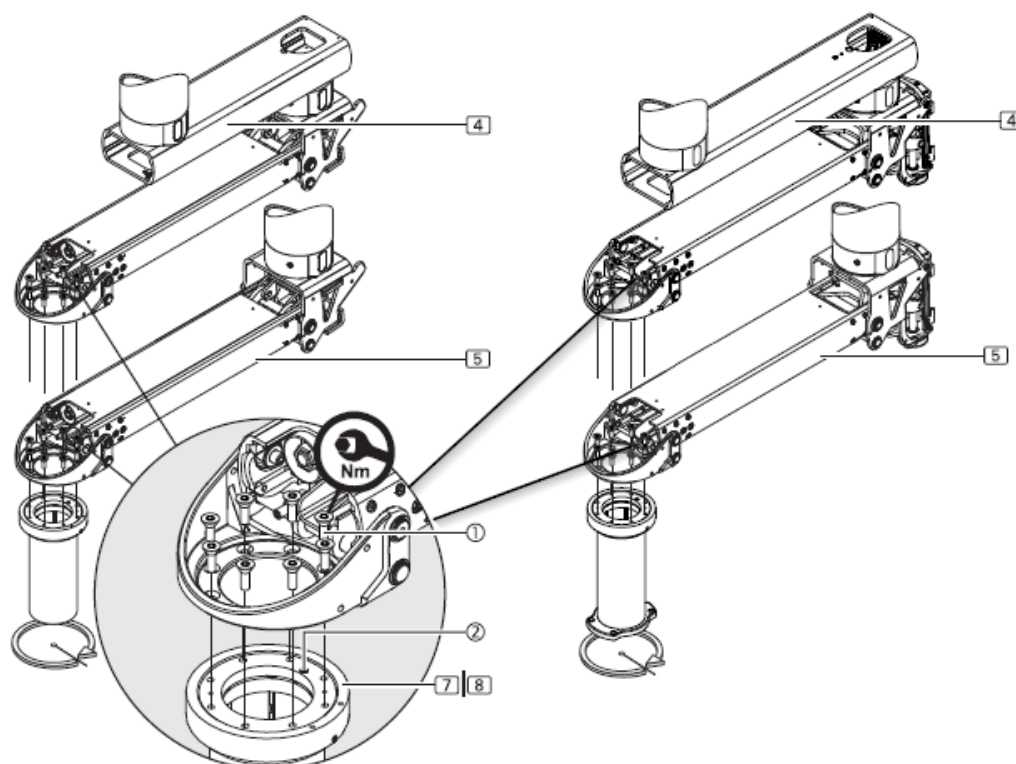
Assemblage du tube de descente sur les bras motorisés et à ressort
